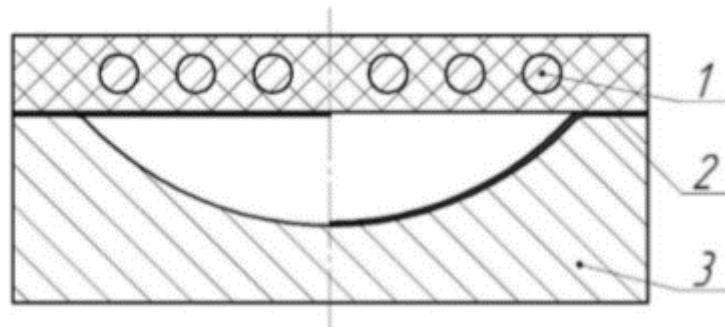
Схема магнітно-імпульсної обробки листового металу: 1 – спіральний індуктор; 2 – листовий метал; 3 – матриця
